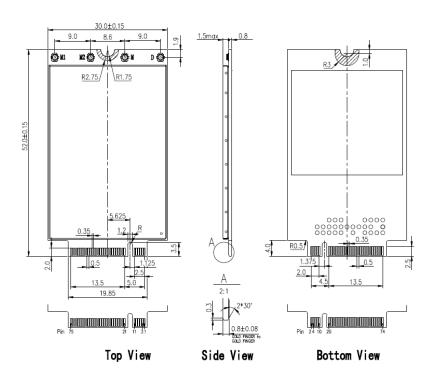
FM650-CN-03/60 结构尺寸(单位: mm)
